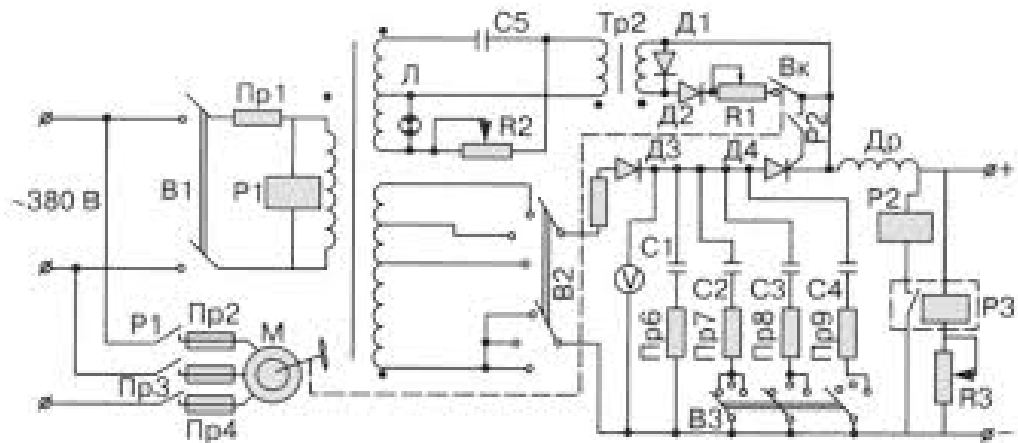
Электрическая схема сварочного выпрямителя ВДУ-1202
